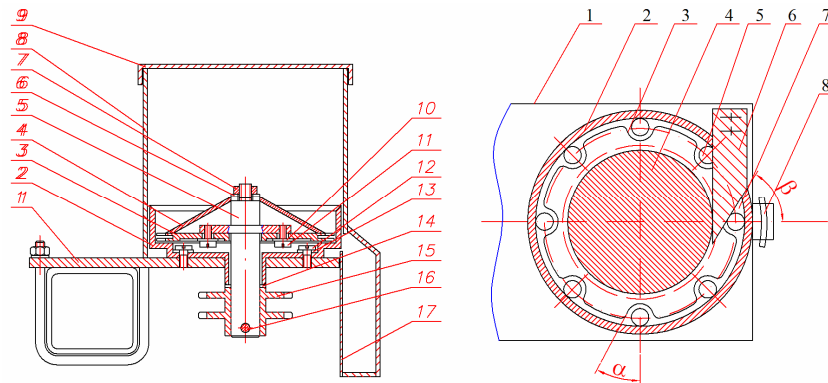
Конструктивна схема апарата точного однозернового висівання насіння [3]
